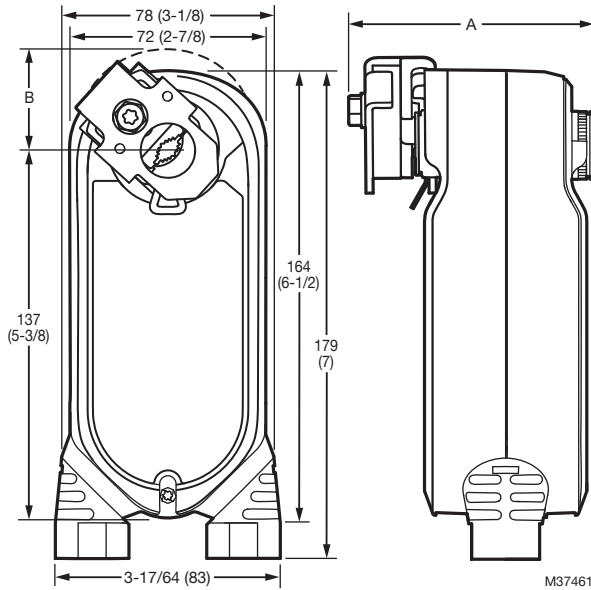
Plano dimensional del actuador en mm (pulgadas). Encontrará las dimensiones A y B en la Tabla 2.
